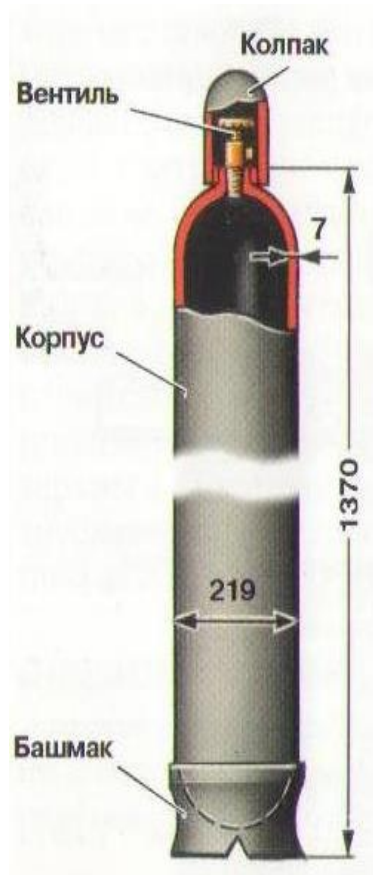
Общий вид стального цельнотянутого баллона, с вентилем и установленным предохранительным колпаком
